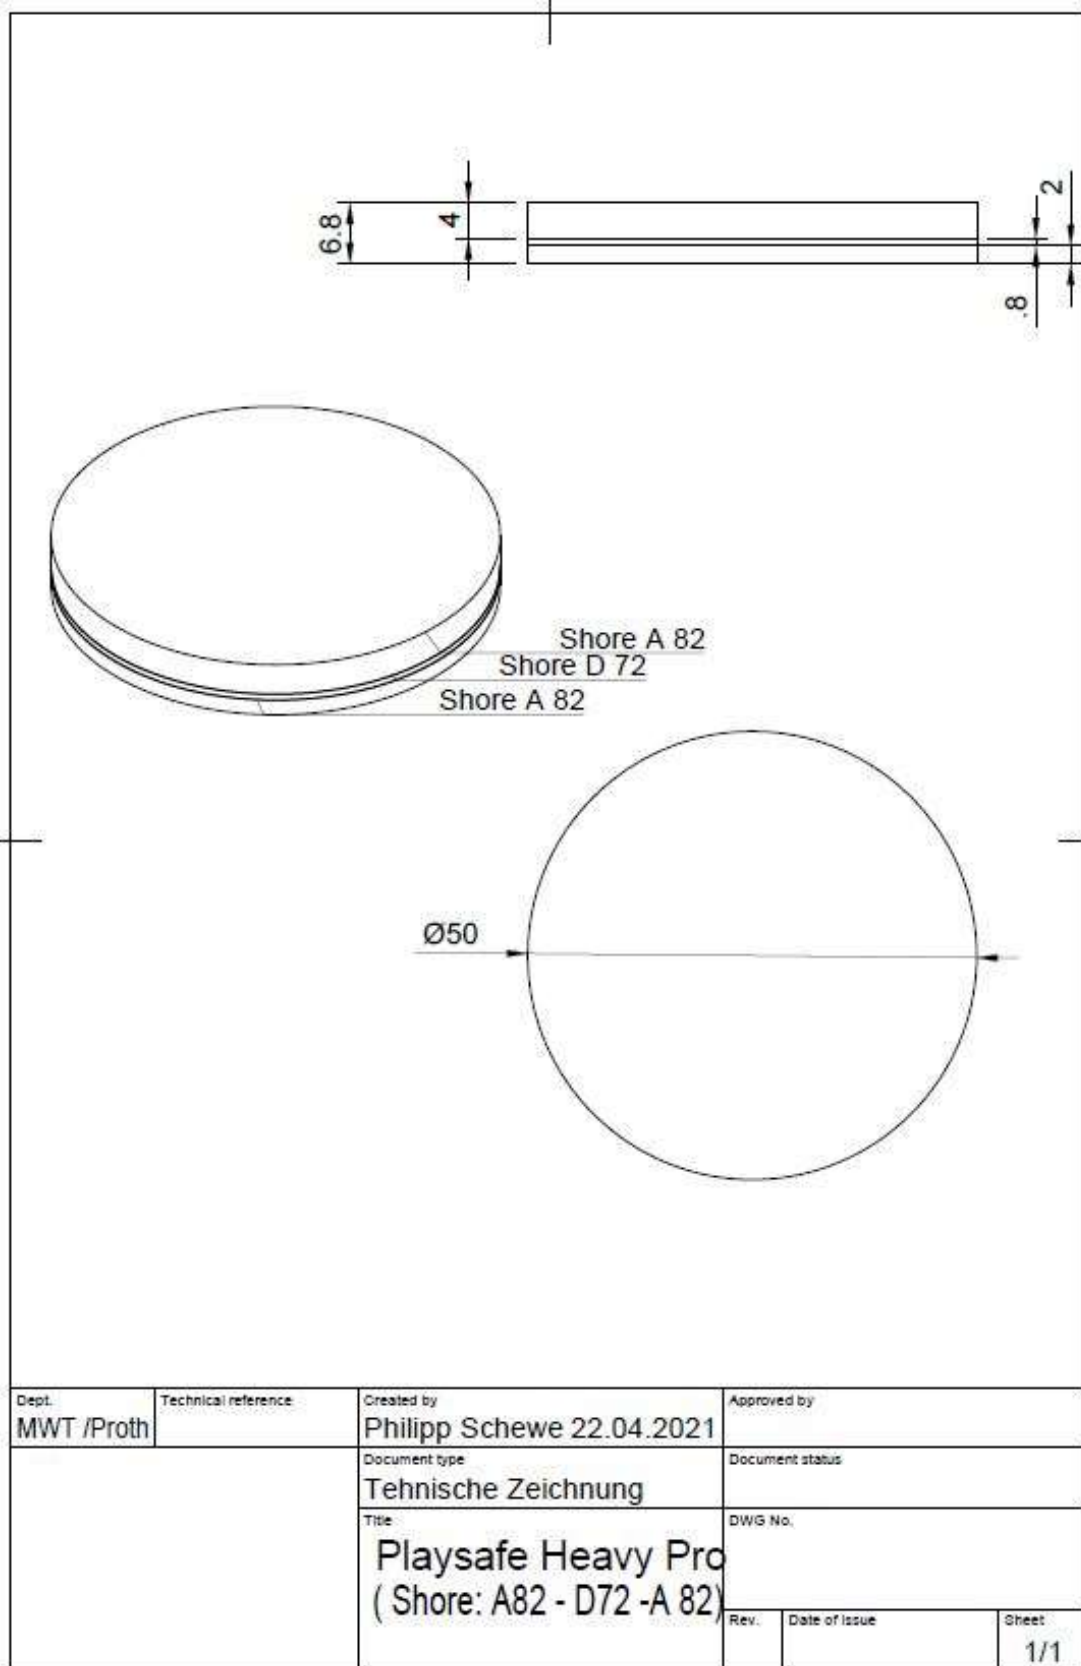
Technische Zeichnung des ER-HP / STR-C
